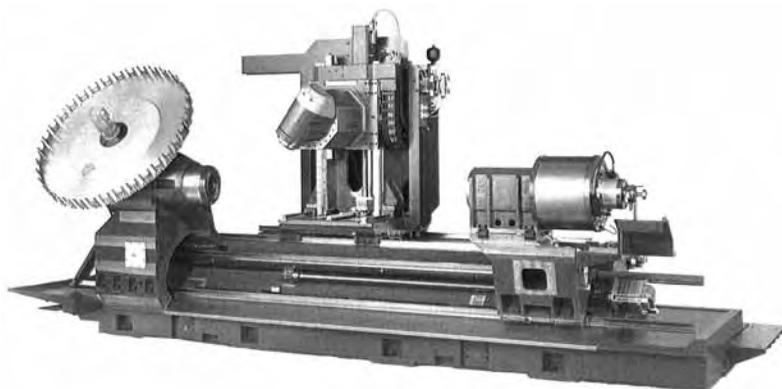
Станок СТХ, оснащенный токарно-фрезерным шпинделем фирмы DMG
